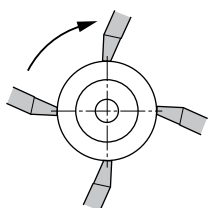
Перевірка аксіального центрування штангенциркулем — контроль під час обертання
